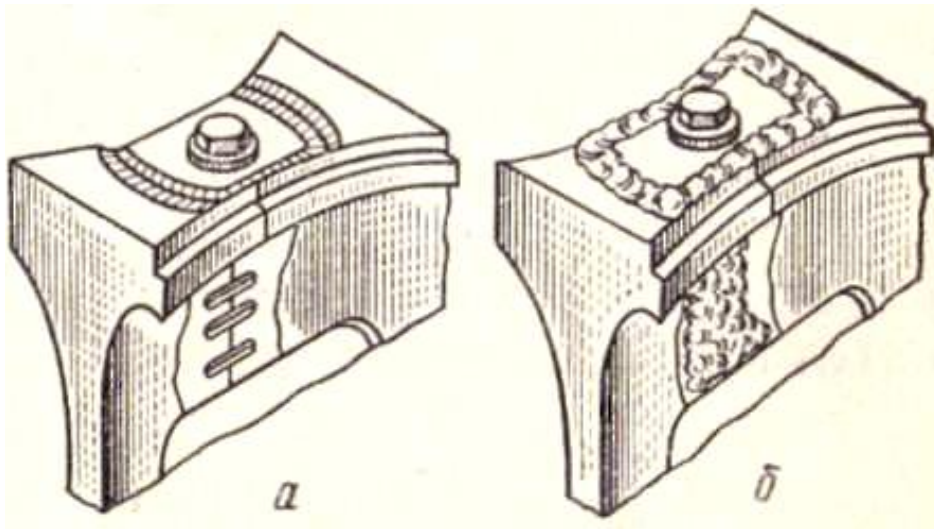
Підготовка тріщини в перемичці між циліндрами до заварки (а) і перемичка після заварки (б).
